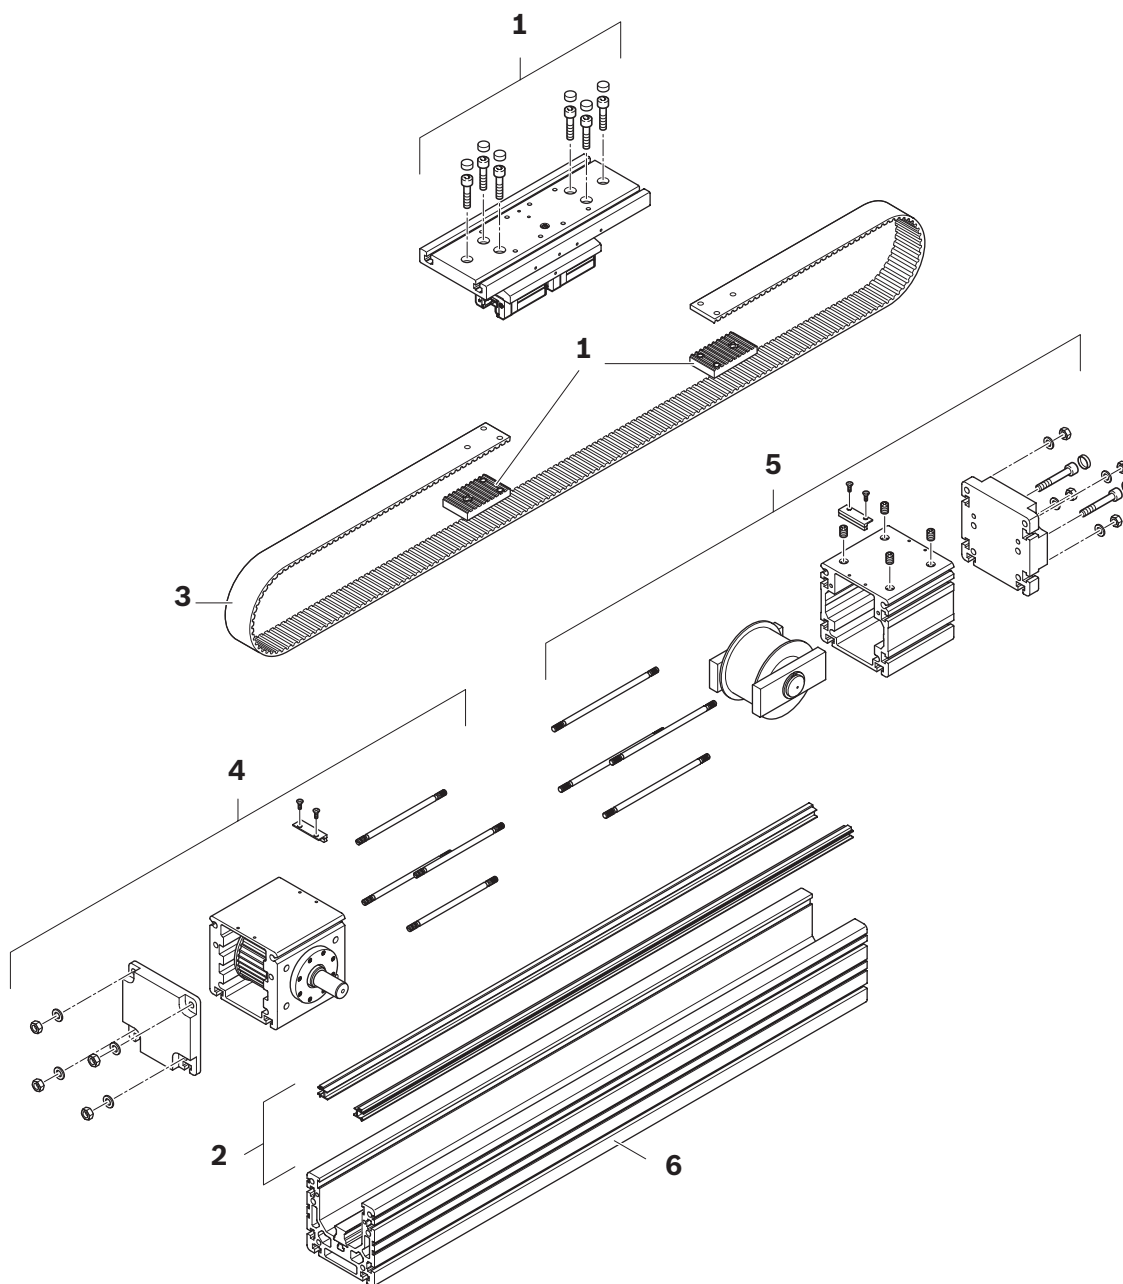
Vue d'ensemble MKR-165-NN-2
